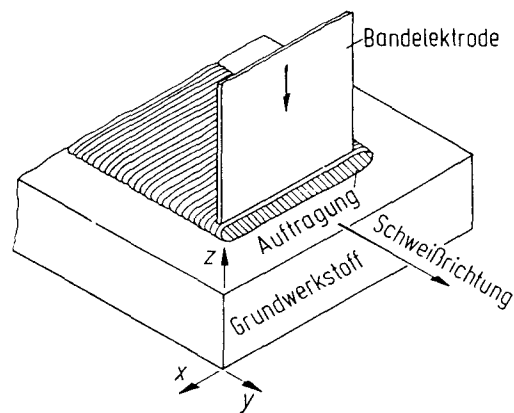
Schweißbadgeometrie und Schweißrichtung beim UP-Bandplattieren
